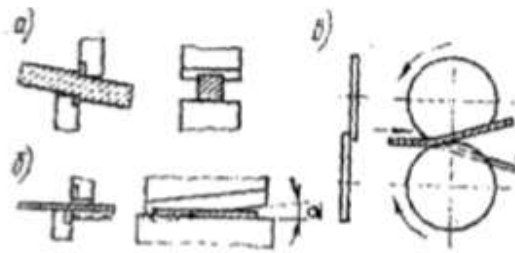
Схема расположения ножей в ножницах: а) с параллельными ножами; б) с наклонным ножом; в) дискового типа.
